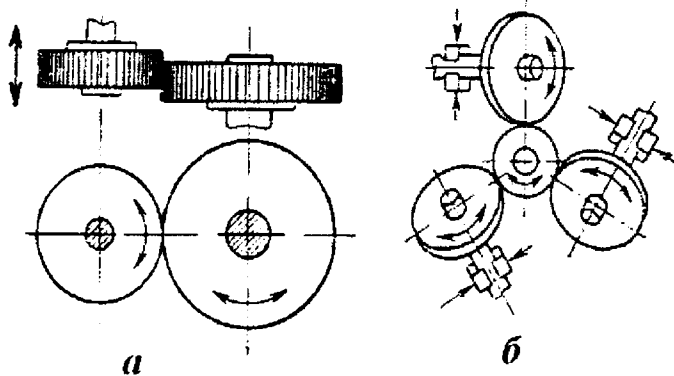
Схемы притирки зубьев цилиндрических зубчатых колес: *а* – с параллельными осями притиров; *б* – со скрещивающимися осями притиров
